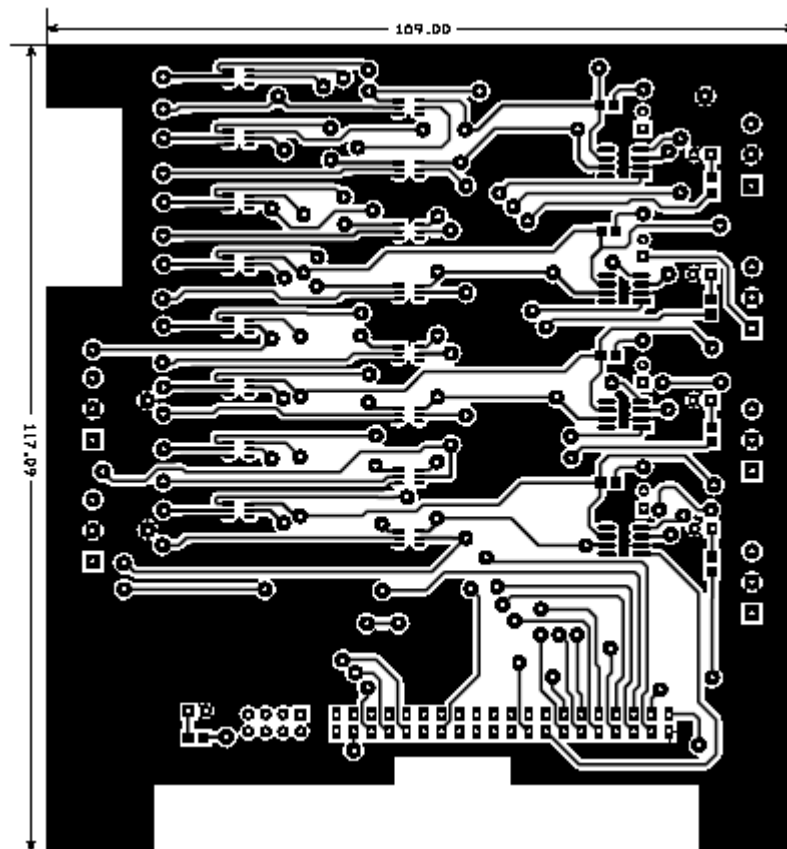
Face de “cima” da PCB (dimensões em milímetros).
